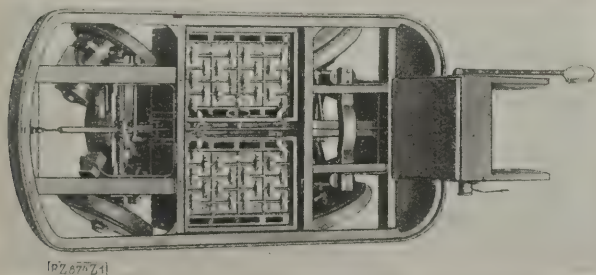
Grundriß des Untergestelles eines SSW-Karrens mit Vierradlenkung.
